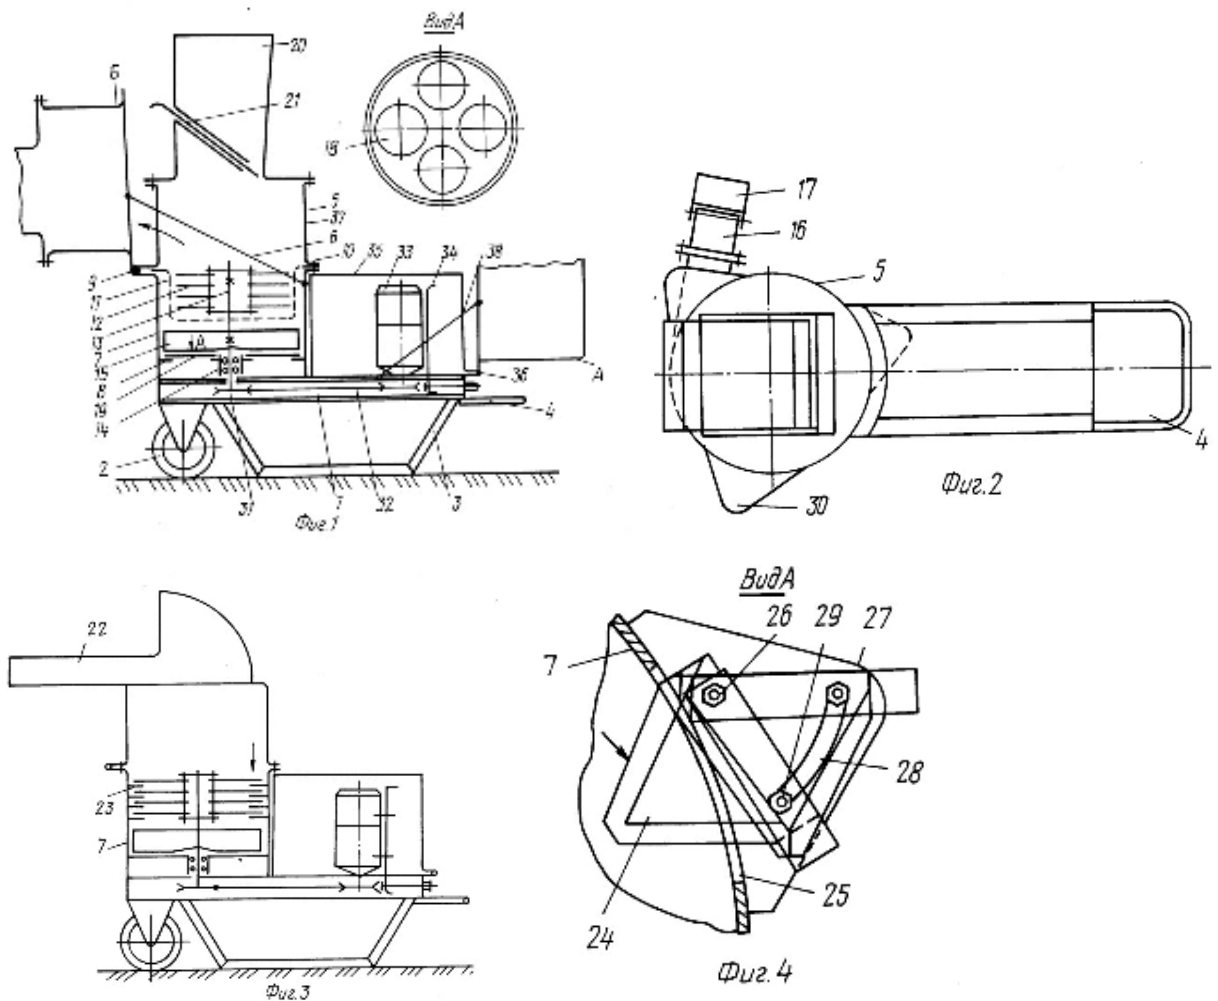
Малогабаритный фермерский измельчитель - смеситель кормов
